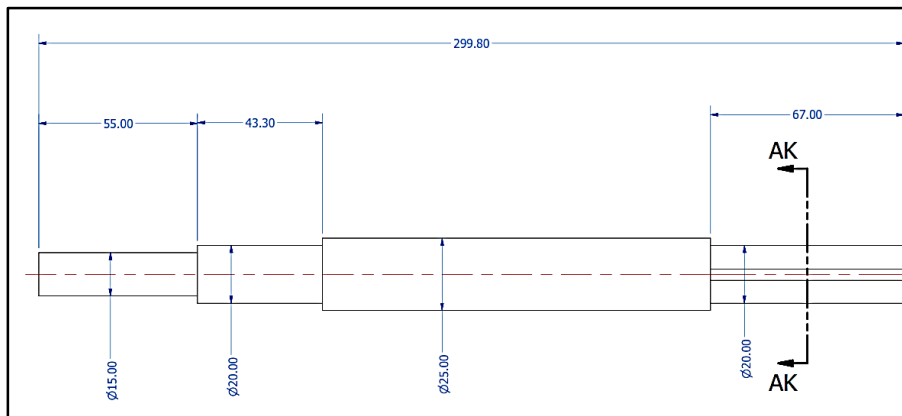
Dimensiones estándares finales del eje de desenrollado de cinta. (Realizado en Inventor®)
